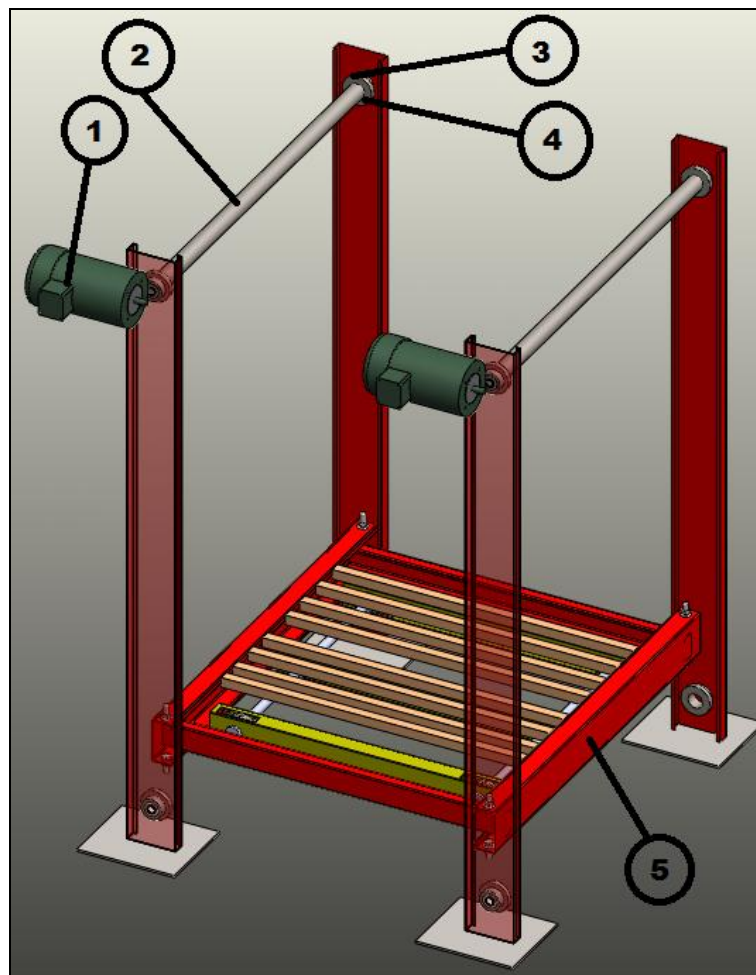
SISTEMA DE ELEVACIÓN DEL PALLET
